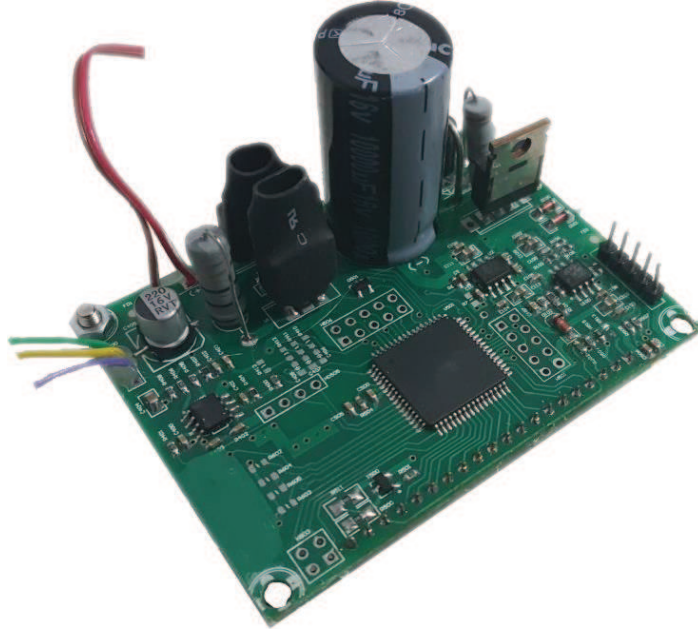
Darbe indüksiyon metal dedektörü PCB tasarımı
